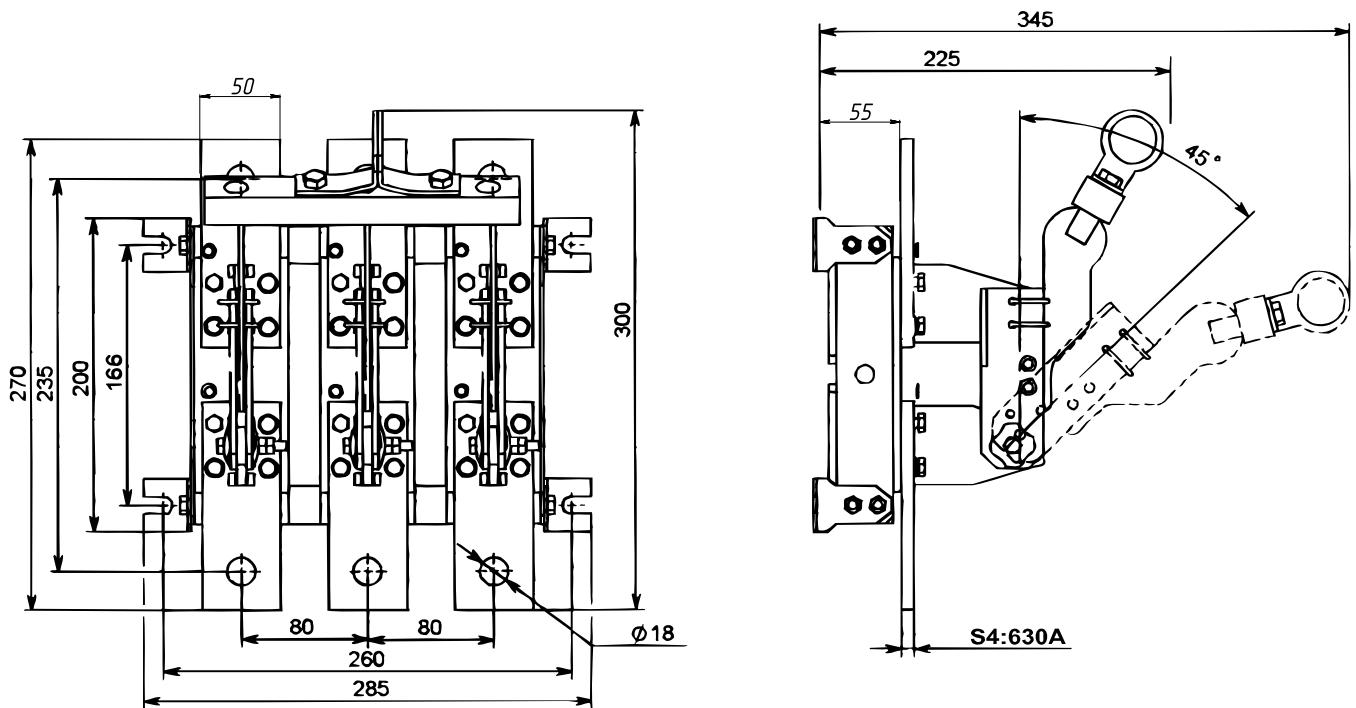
Разъединитель РЕ19-39-31190-00 УХЛЗ с центральным рычагом для управления штангой
